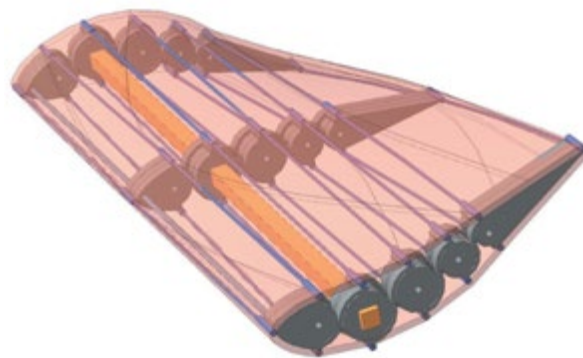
Внешний вид фрагмента адаптивного крыла с обшивкой
